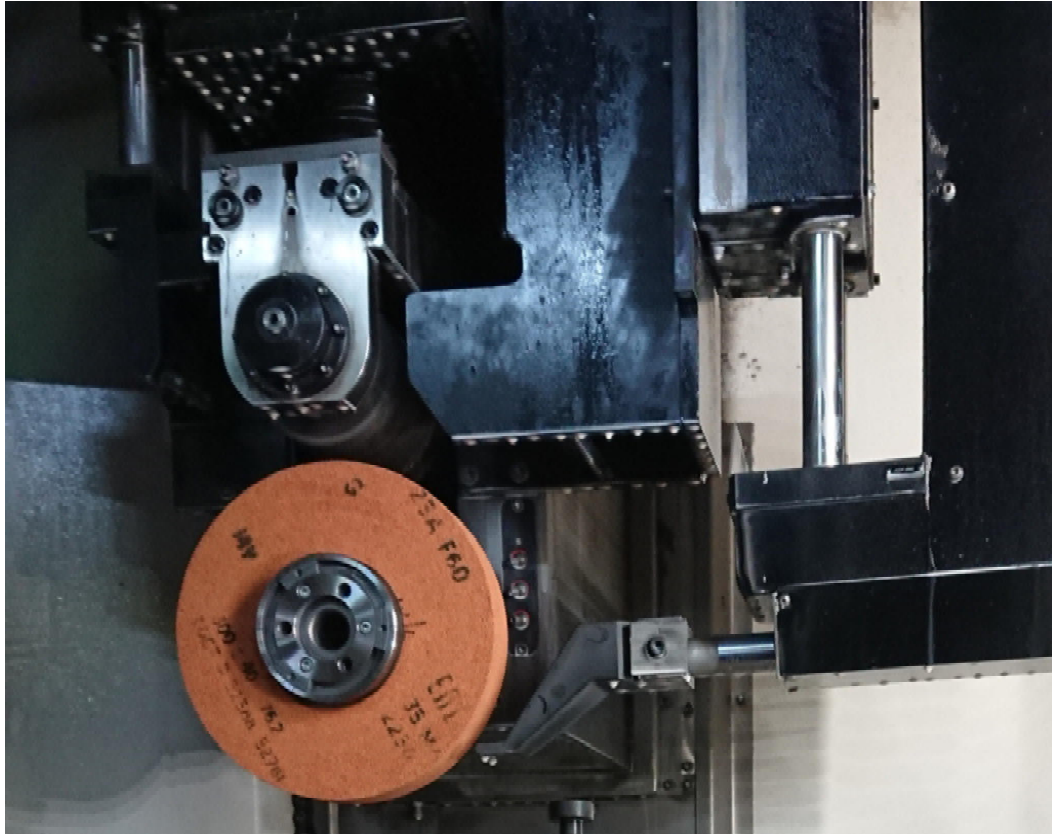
Шлифовальный круг на шпинделе станка и правка алмазным роликом для непрерывной правки
